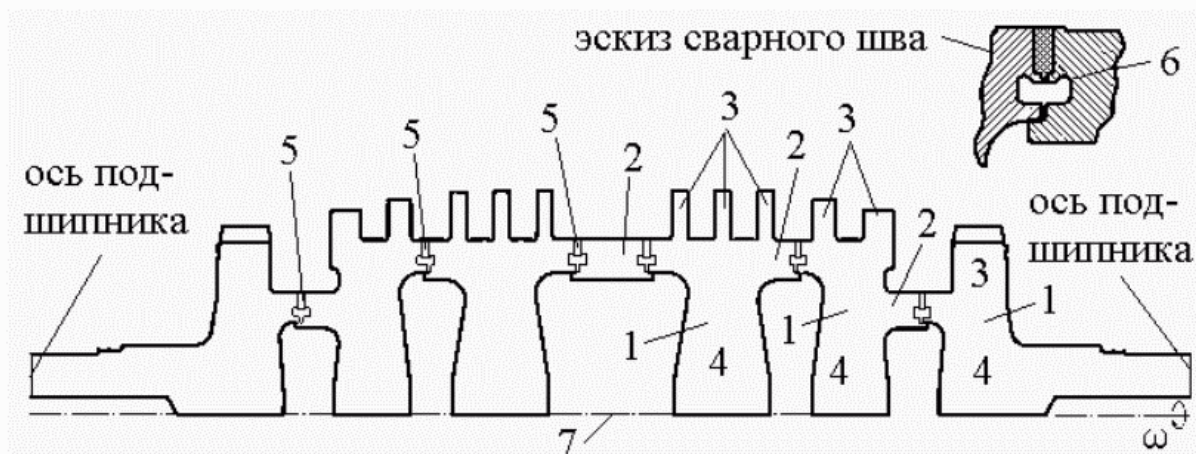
Сварной ротор паровой турбины. 1 - кованые диски; 2 - перемычки; 3 - наружные части дисков; 4 - внутренние части дисков; 5 - сварные швы; 6 "деконцентраторы" напряжений; 7 - ось вращения ротора.
